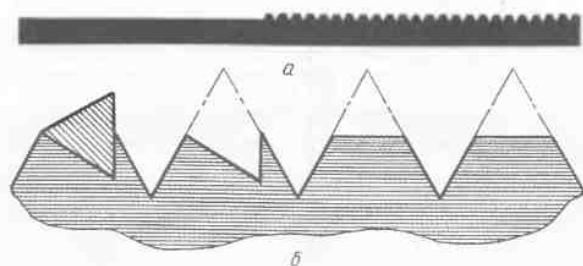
Изготовление пилки: *а* — предварительная обработка заготовки для пилки после отрезания полоски от ножовочного полотна; *б* — деление крупных зубьев на мелкие трехгранным надфилем
